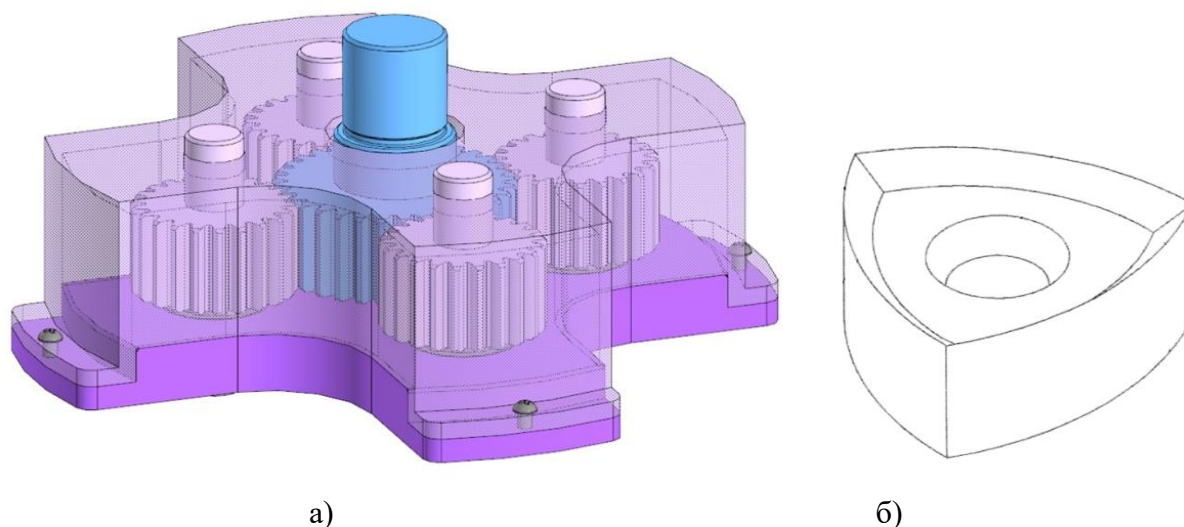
а) фреза с принудительным вращением режущих элементов; б) твердосплавная пластина с РК-профилем
